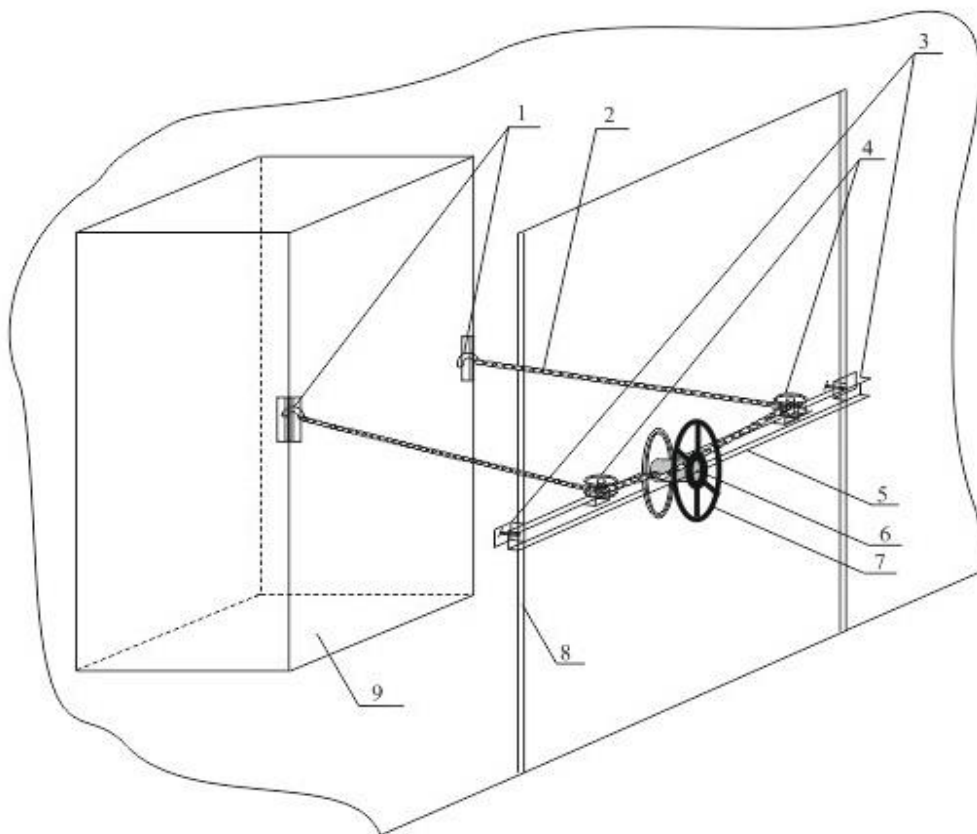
Устройство для перемещения грузов в крытом вагоне
